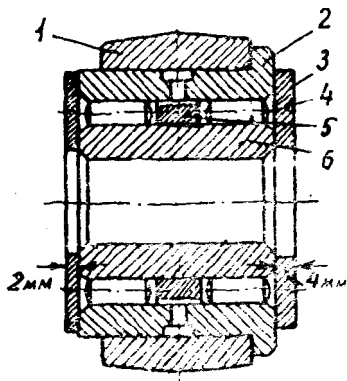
Подшипник рычага клапана: 1—рычаг; 2—наружная обойма; 3—шайба; 4—шпиль; 5—ограничительное кольцо; 6—внутренняя обойма подшипника
